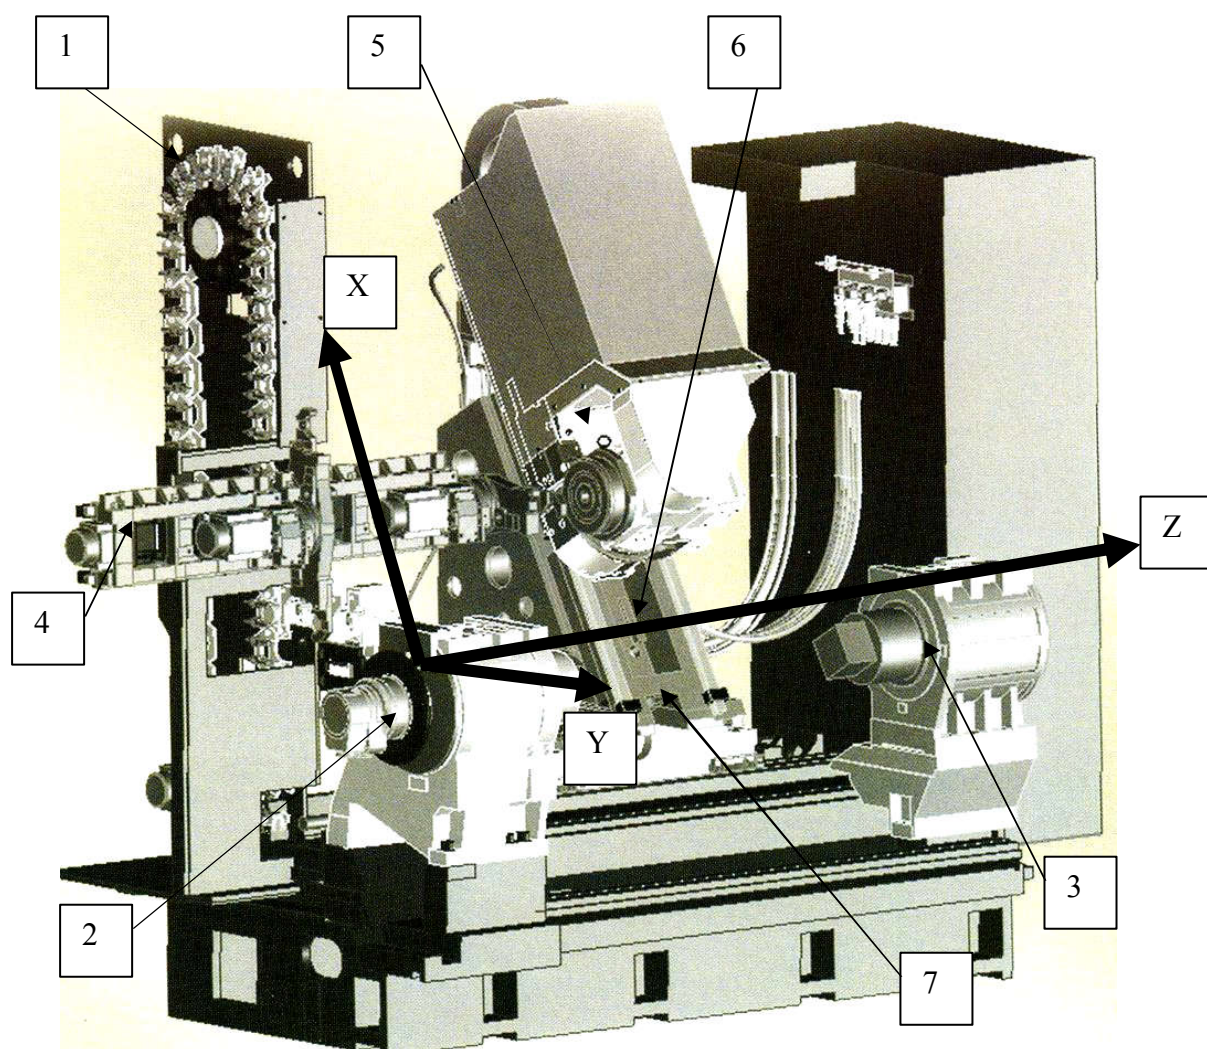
Схема токарно-фрезерного обрабатывающего центра
